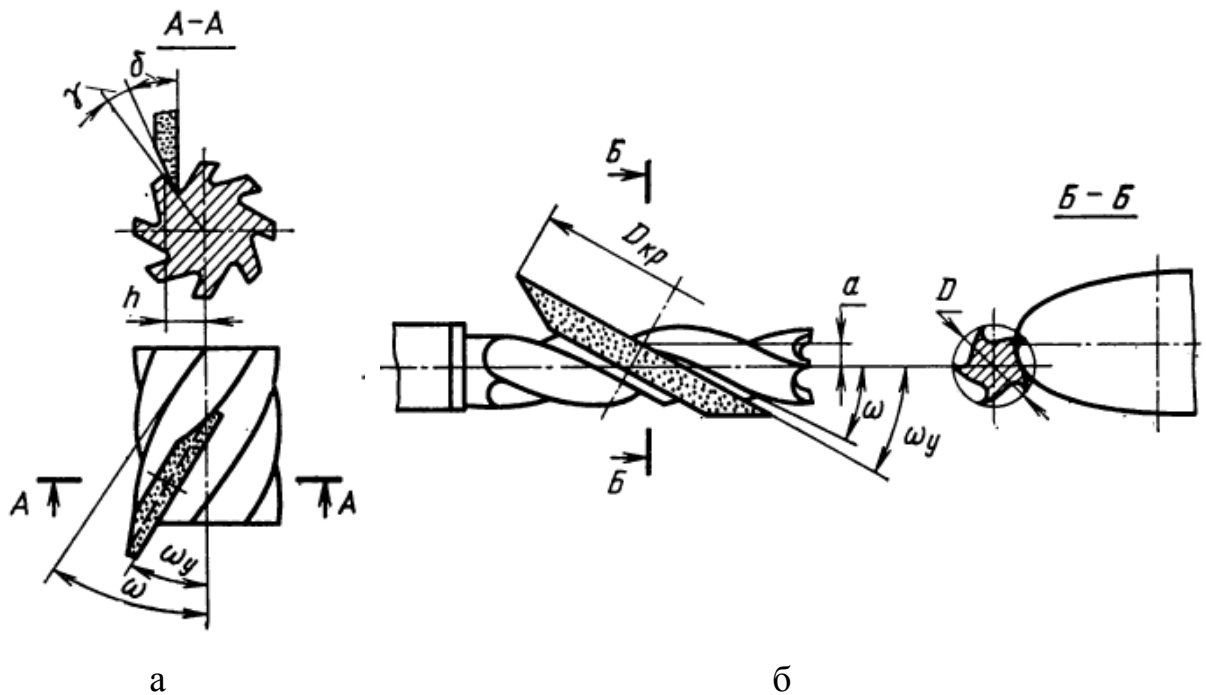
Схема заточки передньої поверхні гвинтових зубців фрези:
